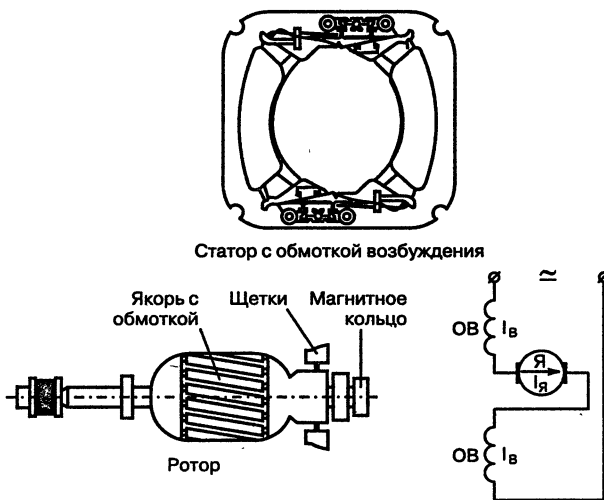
Устройство и принципиальная схема коллекторного двигателя
